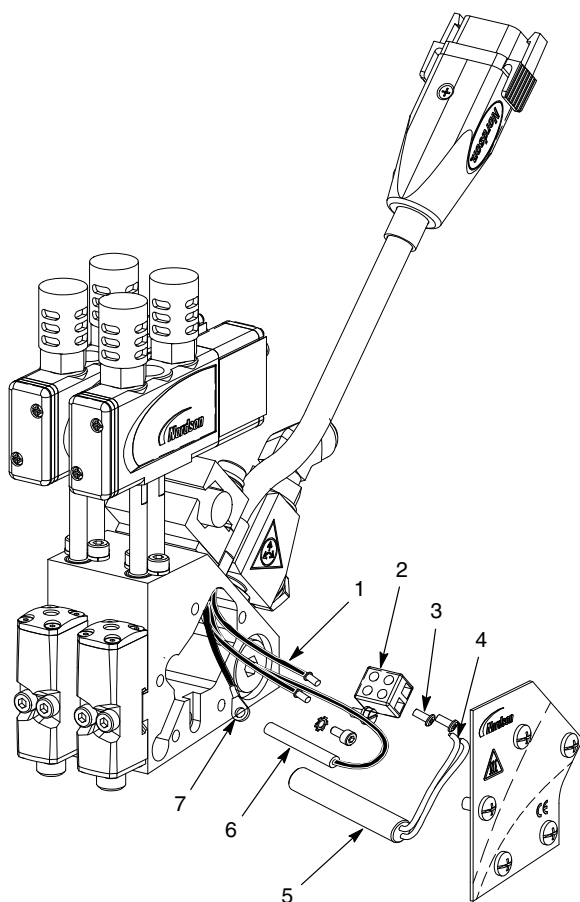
Remplacement d'un élément chauffant ou d'une sonde RTD sur un applicateur mono-module large ou multi-modules configurable
